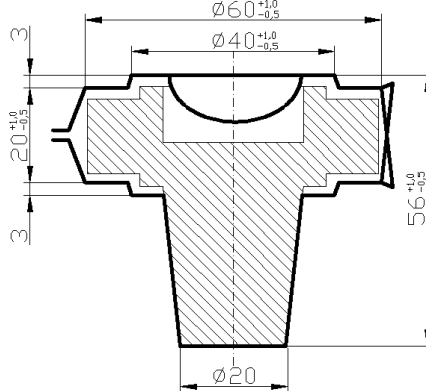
Эскиз поковки. Слева от осевой линии – для облойной штамповки, справа – для безоблойной штамповки.
